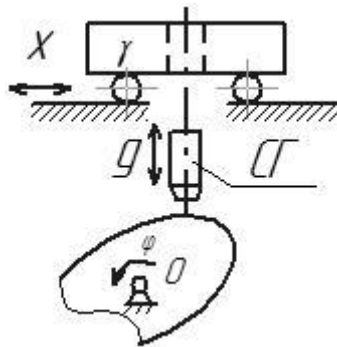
Спосіб автоматичного зварювання поворотних деталей з горизонтальним розташуванням зварювальної ванни
